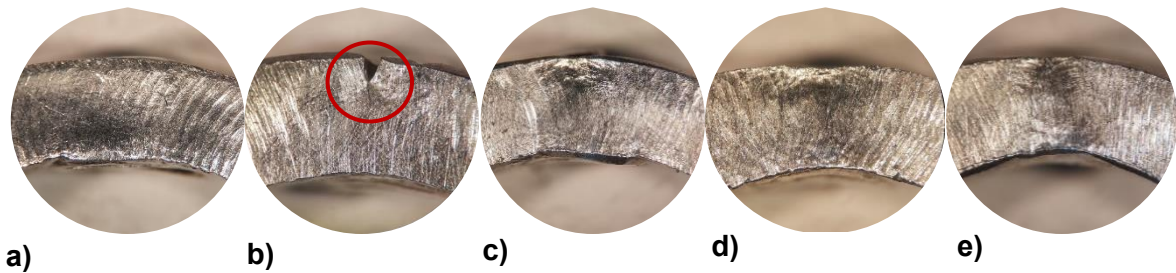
Ensayo de doblado en soldaduras AISI 304 con material de aporte ER 308L: a) 70 A; b) 80 A; c) 90 A; d) 100 A; e) 110 A
